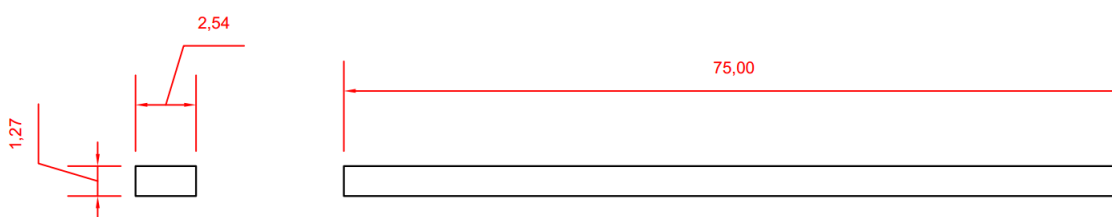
Dimensões em centímetros da viga retangular a ser usada nos ensaios
